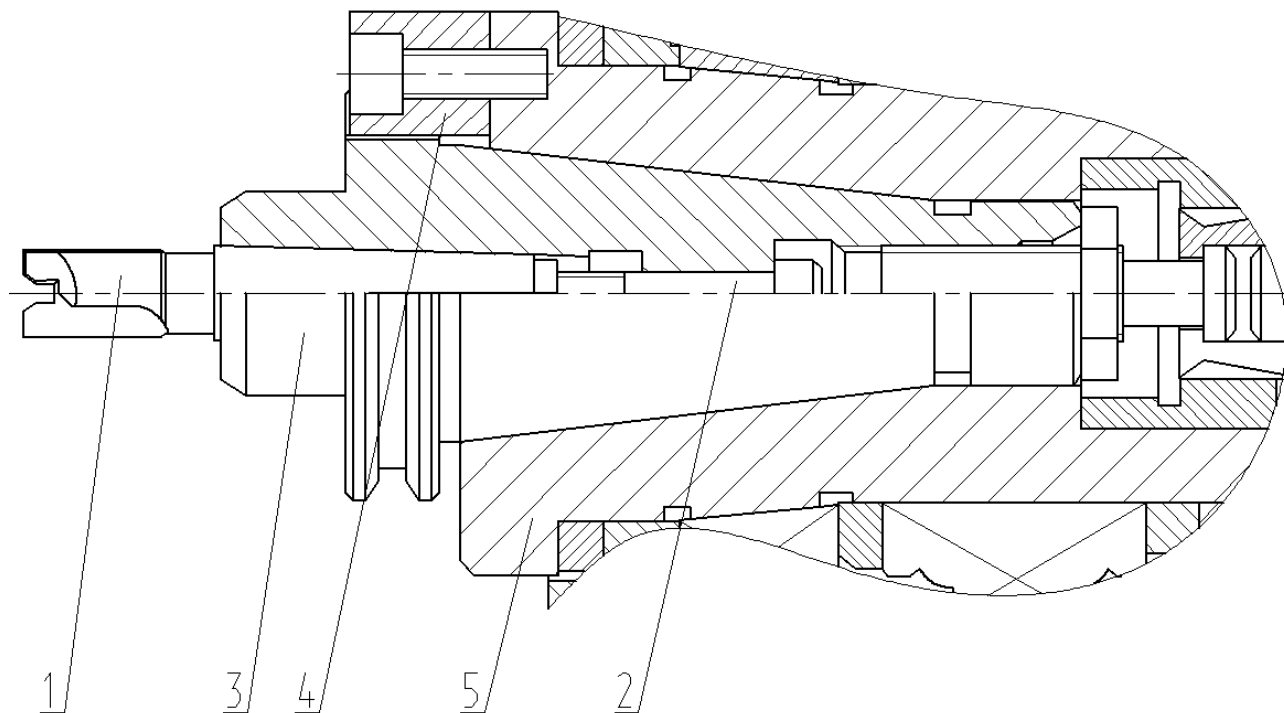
Фрагмент шпиндельного узла сверлильного станка.
